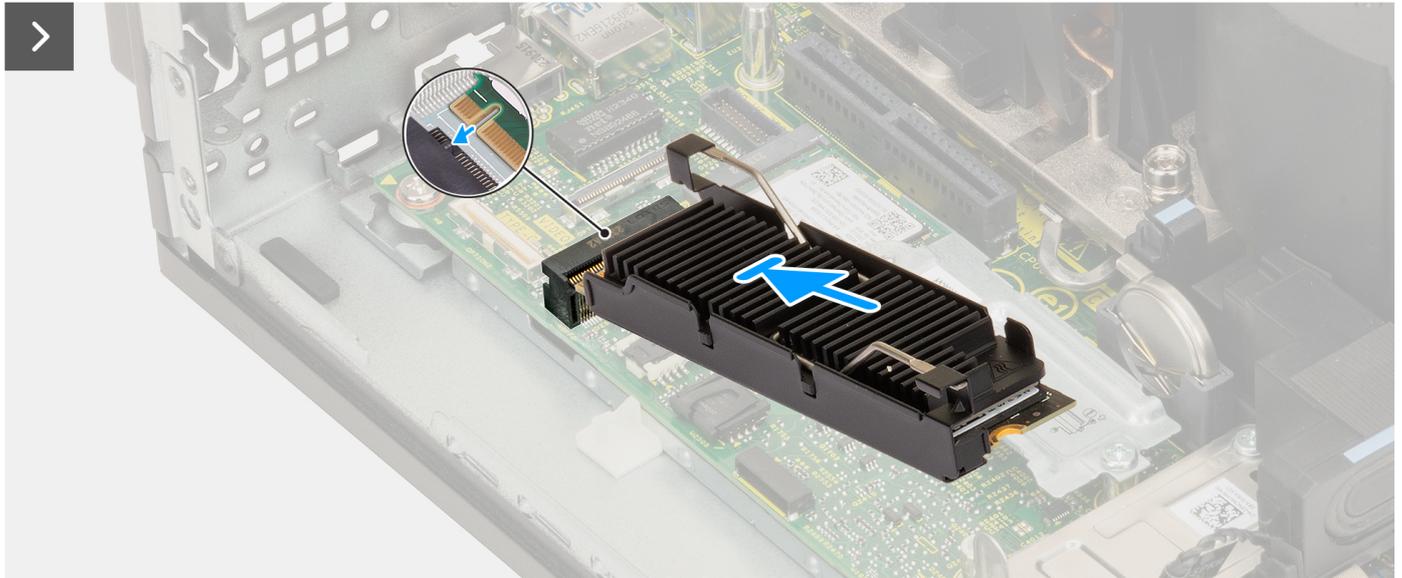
Einbauen des M.2 2280-PCIe-SSD-Laufwerks (Steckplatz 2) mit Kühlkörpermodul
